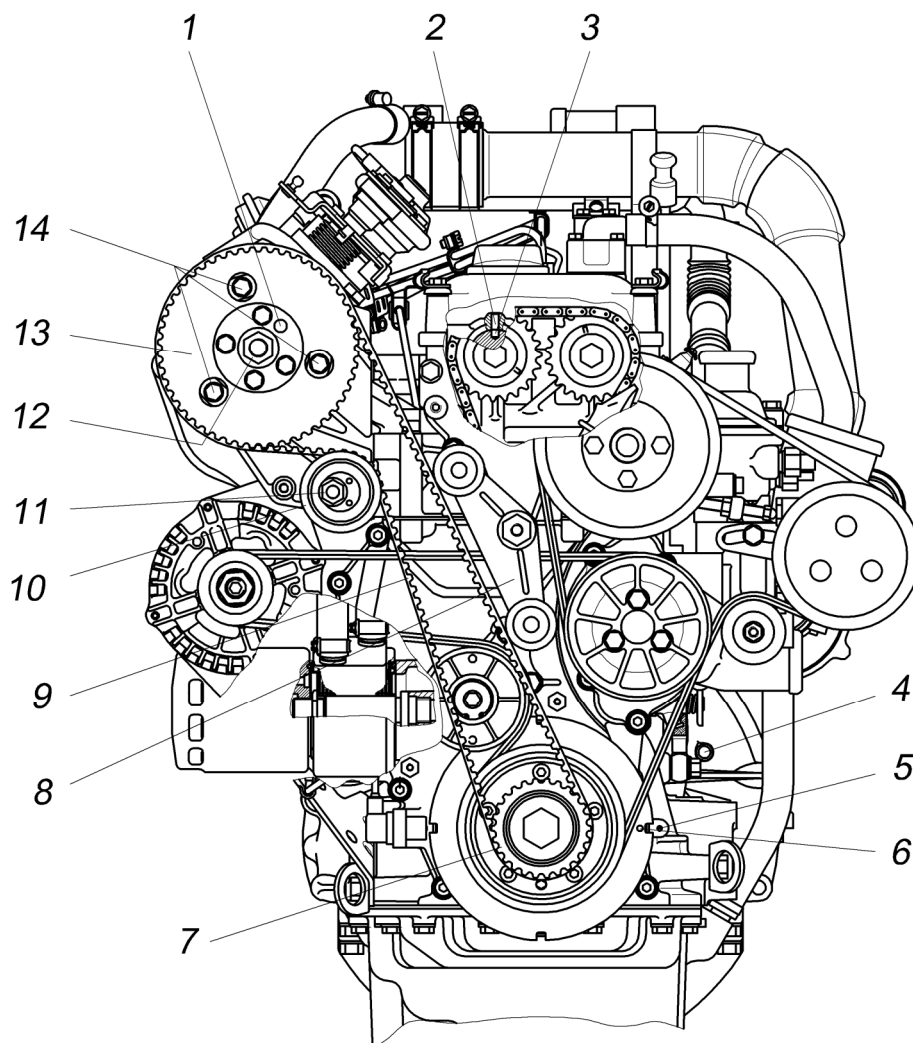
Расположение меток и отверстий под штифты для замены ремня привода ТНВД:
